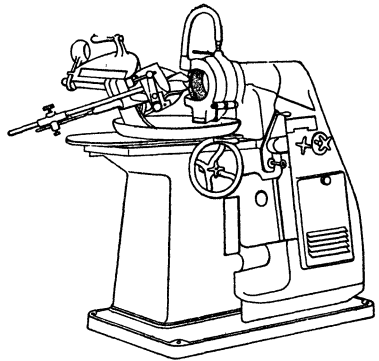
Spiralbohrerschleifmaschine für Bohrer von 10 bis 75 mm Durchmesser. Bauart R. Stock & Co., Berlin-Marienfelde.
